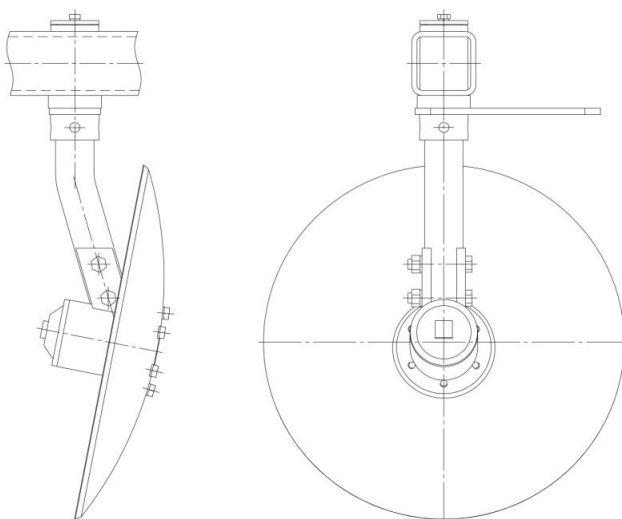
Рабочий орган дисковых борон с жестким креплением к раме
